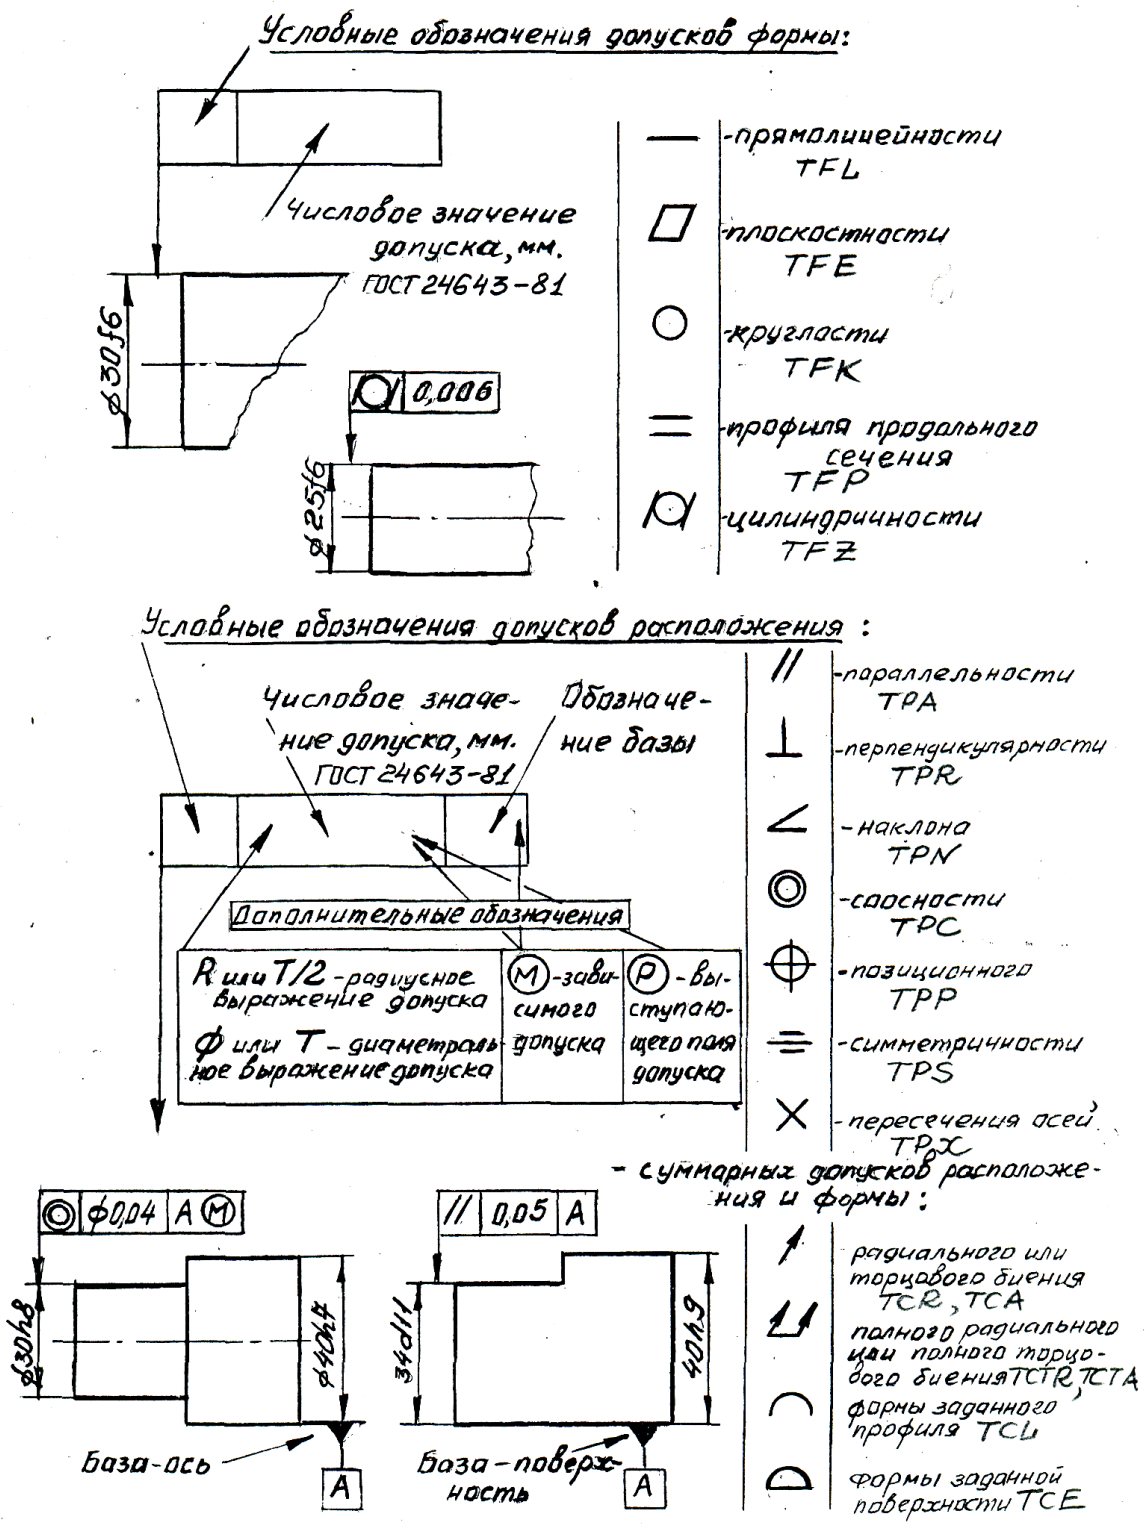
Допуски формы и расположения поверхностей
